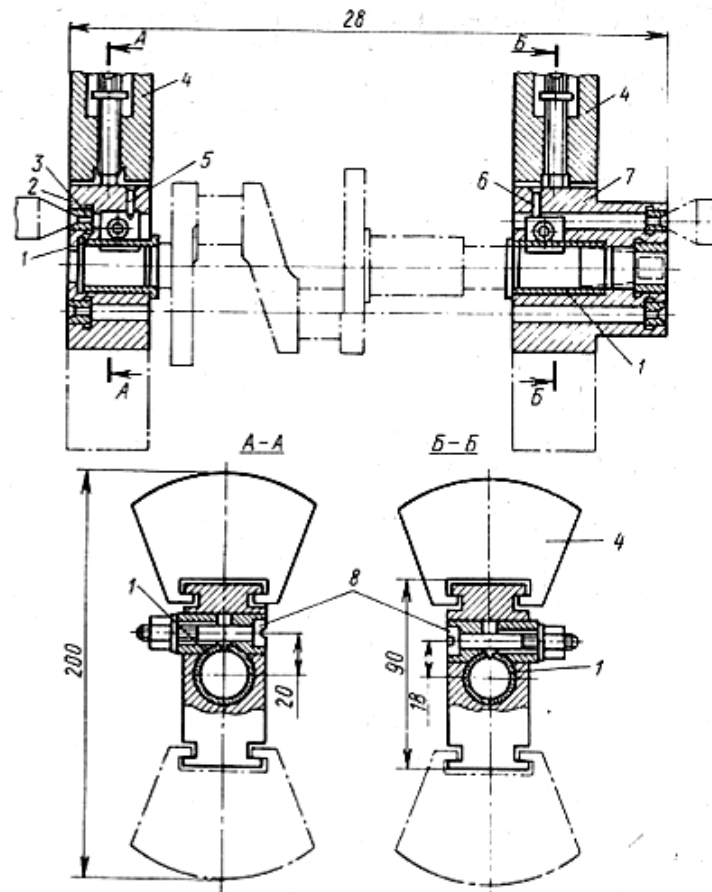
Бугели для шлифовки шеек коленчатого вала:
